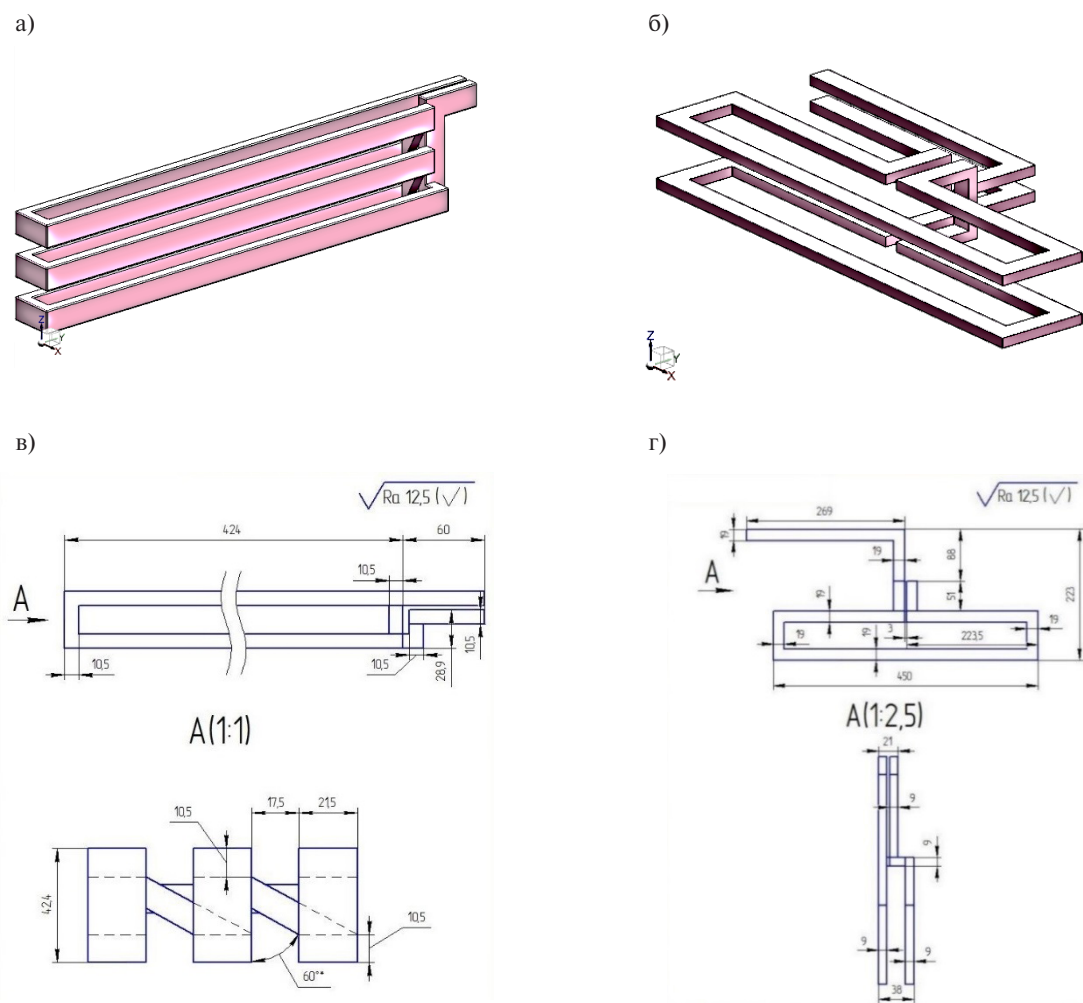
Конструкции индукторов для обеспечения локального нагрева в а) продольном и б) поперечном магнитном поле
